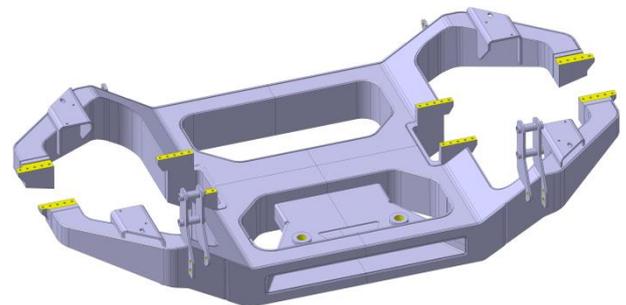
Radträgerschweißbaugruppe mit bearbeiteten Anbindungsflächen (gelb)
